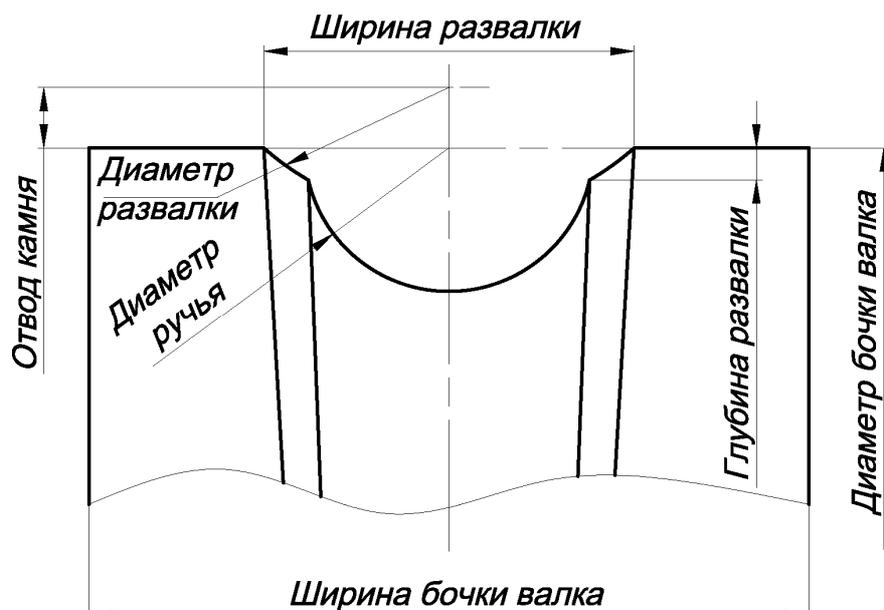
Схема валкового инструмента для процесса периодической прокатки труб
